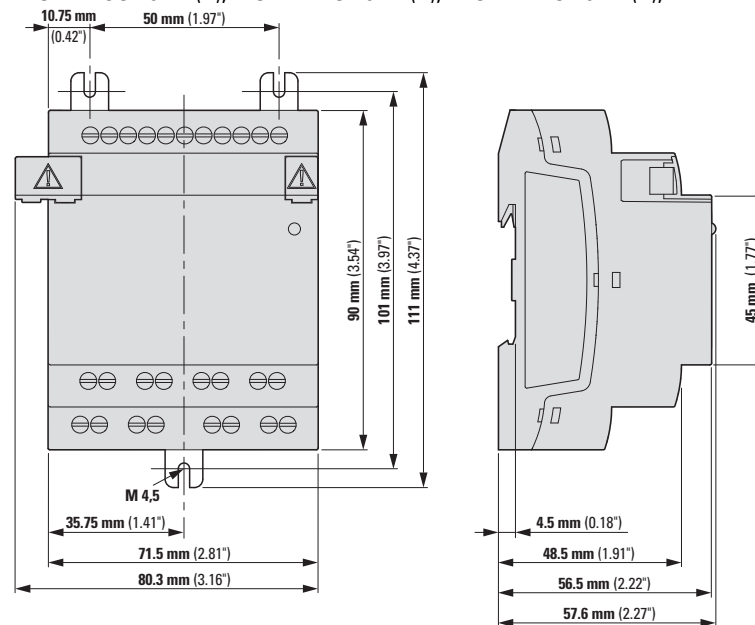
Dimensions en mm (pouces) extensions 4 PE
